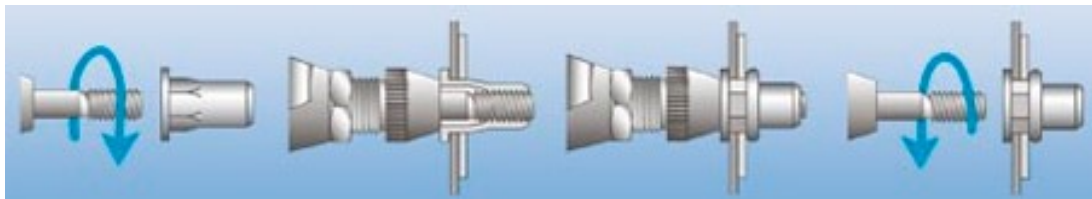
Процес установки бонки в тонкостінні деталі [11]
